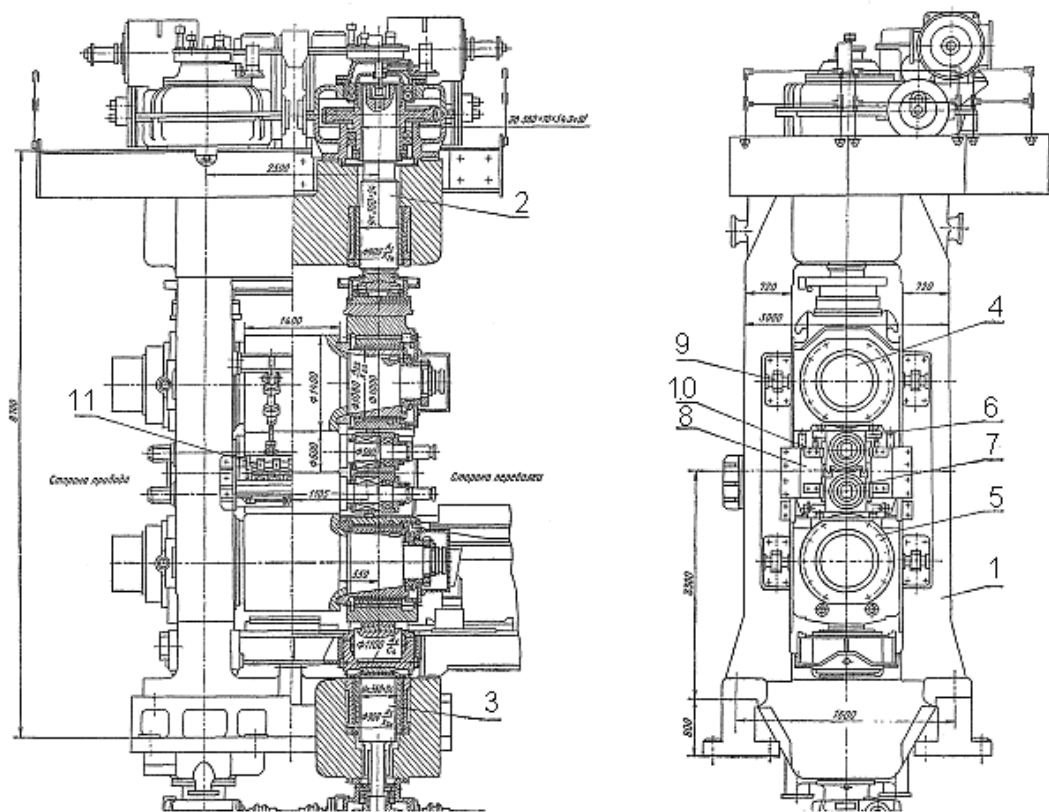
Робоча кліть реверсивного стана 1200: 1- станина; 2 – верхній натискний механізм; 3 – нижній механізм для встановлення валків; 4 – верхні подушки опорних валків; 5 – нижні подушки опорних валків; 6 – верхній робочий валок з подушками; 7 – нижній робочий валок з подушками; 8 – вставки-упори у вікнах станини; 9 – гідрофіксатори опорних подушок; 10 – гідрофіксатори робочих подушок; 11- плоский провідковий стіл
